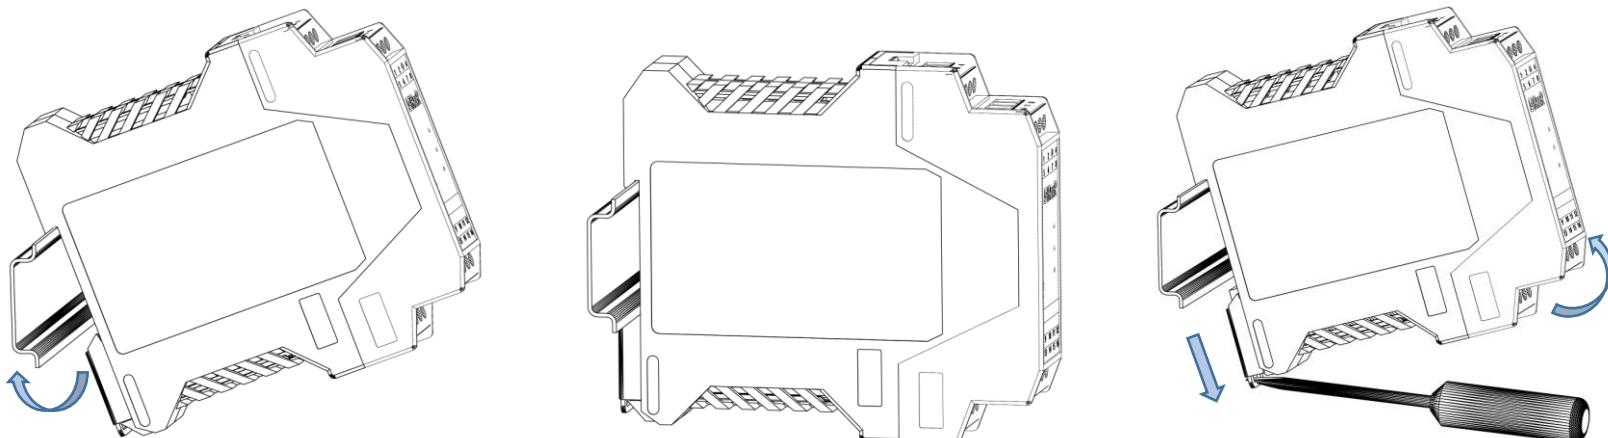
Montaggio-smontaggio meccanico / Mechanical assembly-disassembly
